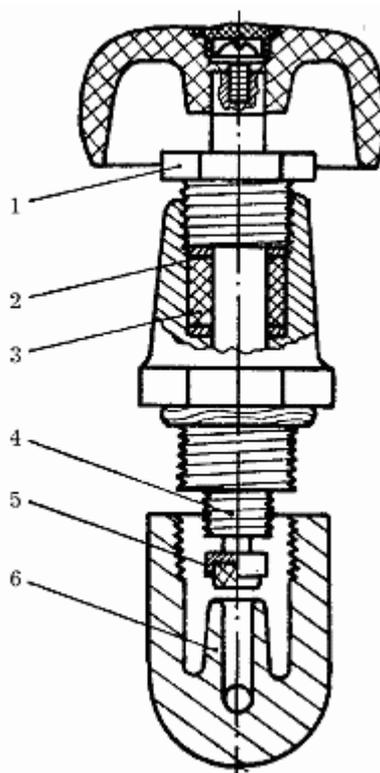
Головка крана: 1 – втулка; 2 – шток; 3 – набивка сальника; 4 – резьба штока; 5 – клапан с прокладкой; 6 – седло клапана.
